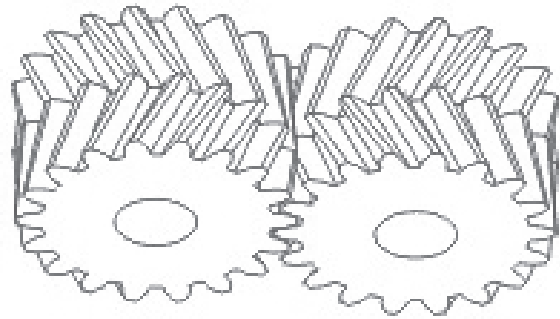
Внешний вид цилиндрической передачи с тормозящим профилем в шевронном исполнении
